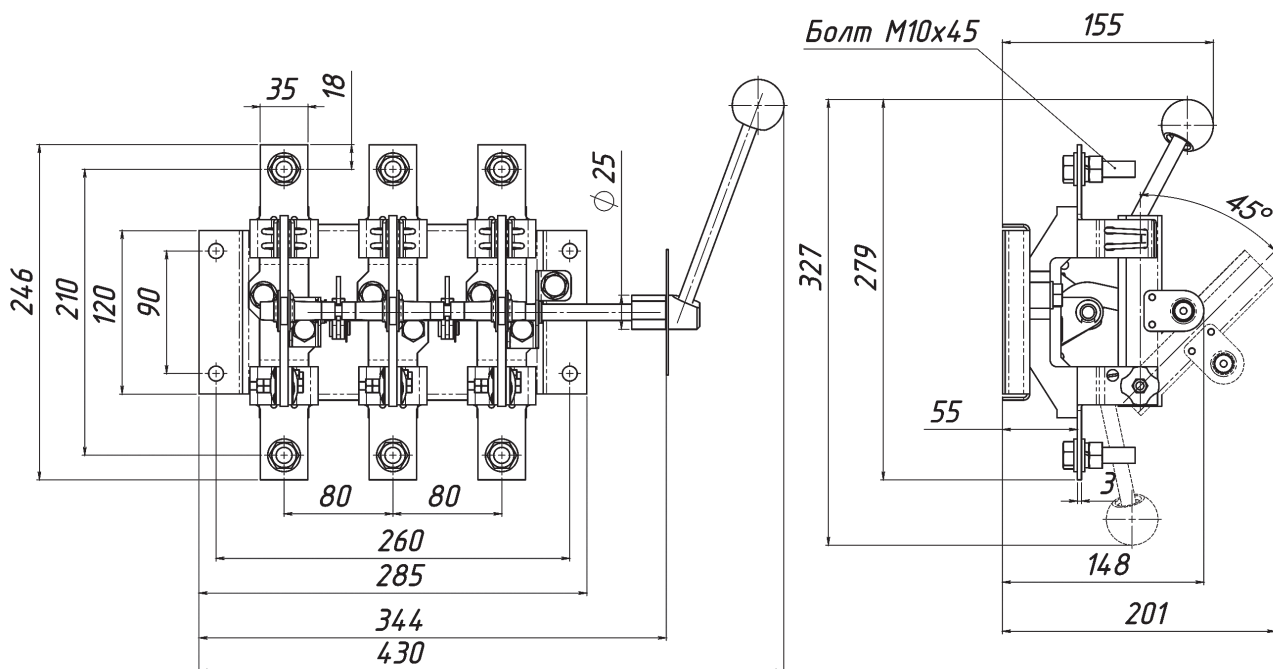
Разъединитель серии Р с боковой рукояткой РБ-6, на номинальный ток 630 А
